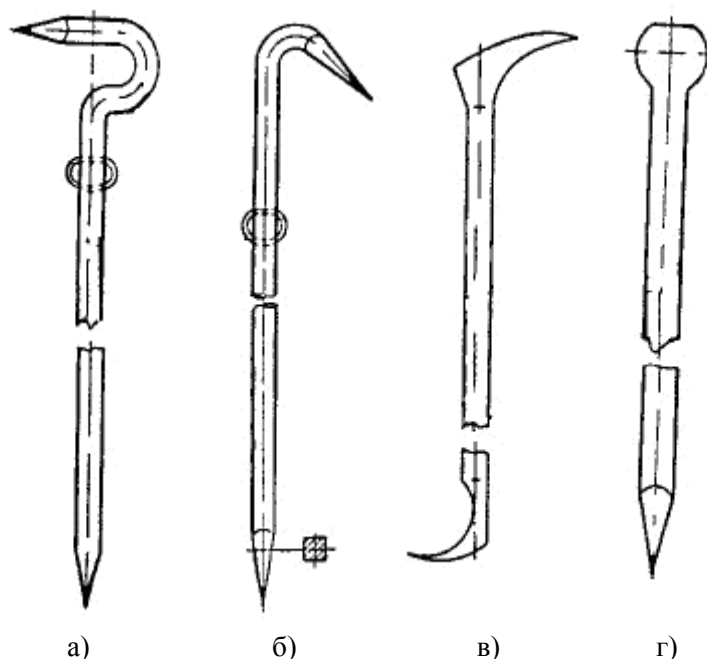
Пожежні лом: а) лом пожежний важкий; б) лом пожежний легкий; в) лом пожежний універсальний; г) лом з шаровою головою
